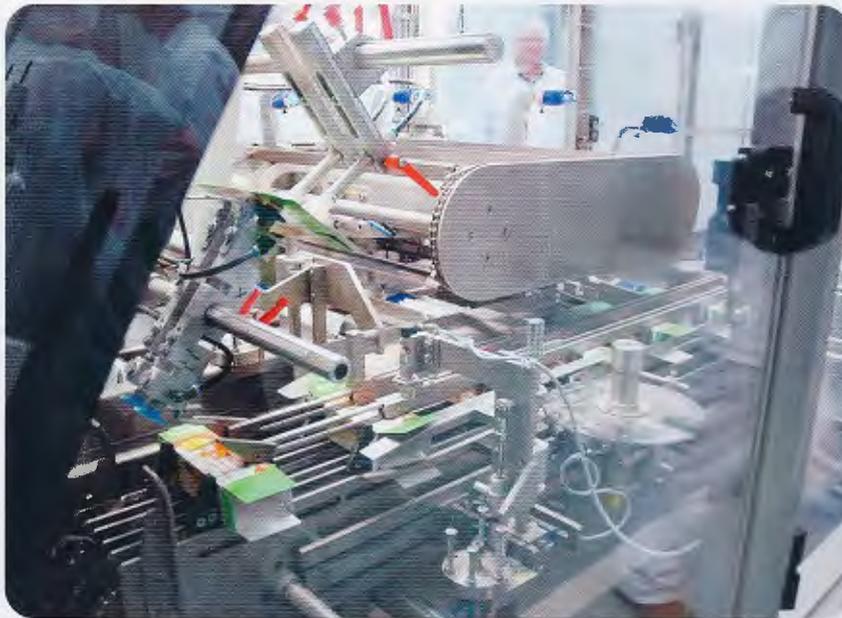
Ein komplexer Mechanismus mit Saugnapfen entfaltet die Verkaufsverpackungen und platziert sie auf der Fördereinrichtung. Ohne Halt werden die Riegel seitlich in die einseitig geöffneten Schachteln geschoben.
